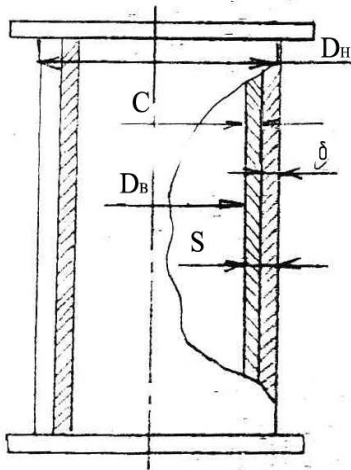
Розрахунок товщини стінки корпусу
